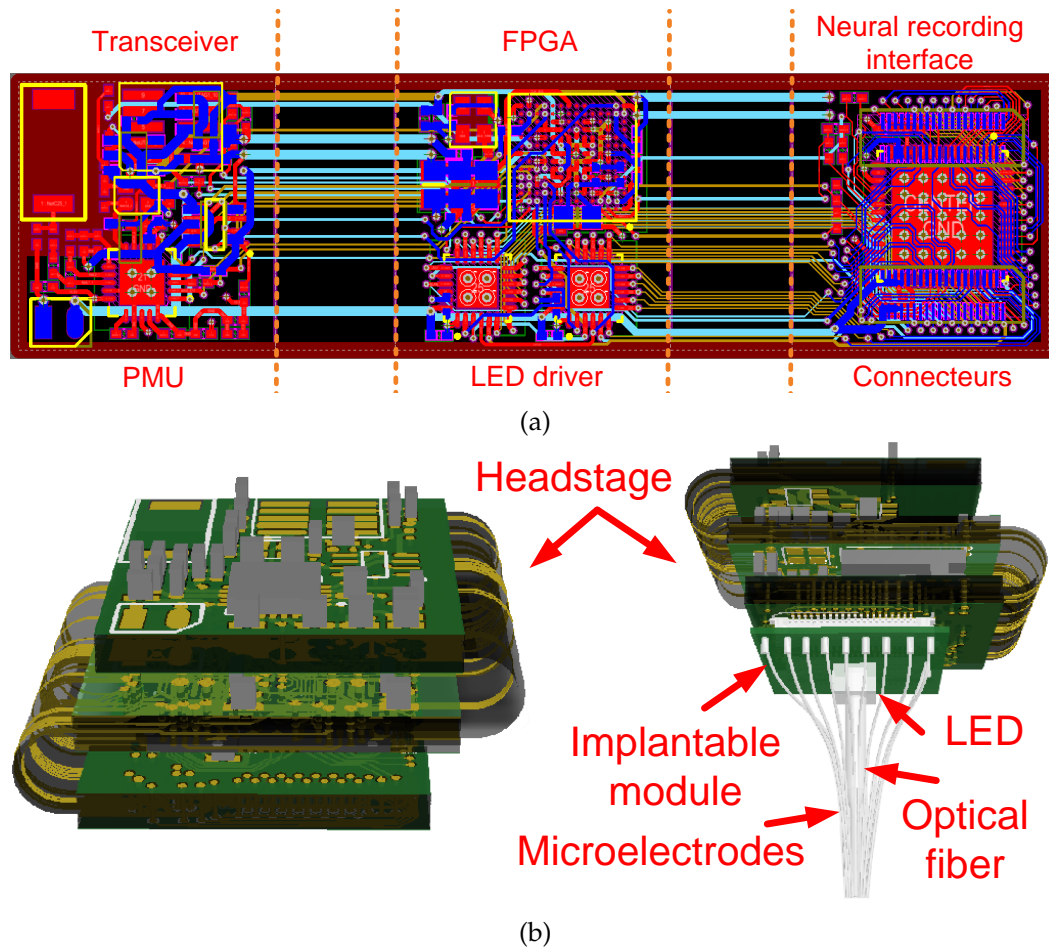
a) Design du PCB flexible rigide, b) vue 3D du PCB flexible rigide déplié, c) vue 3D du PCB flexible rigide replié et attaché à un module implantable montrant une DEL couplée à une fibre optique et 9 microélectrodes.
